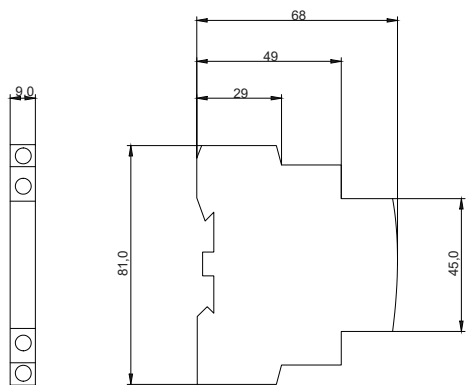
Габаритные размеры дополнительных контактов типа 1НО, 1НЗ, 2НЗ и 2НО / Figure 7 – Dimensions of auxiliary contacts of 1NO, 1N3, 2N3 and 2NO types
